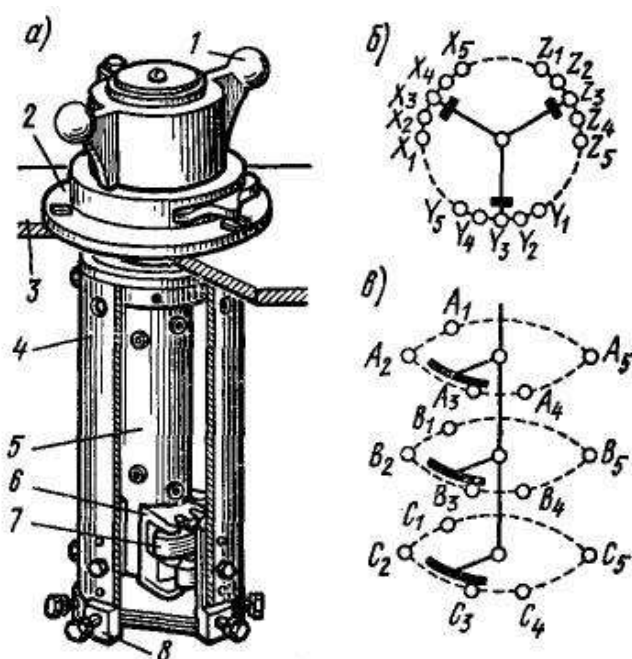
Трехфазный переключатель ответвлений (а) и схемы расположения его контактных элементов (б, в): 1 — привод, 2 — фланец колпака; 3 — крышка бака трансформатора; 4 — бумажно-бакелитовый цилиндр; 5 — бумажно-бакелитовая изоляция вала; 6 — коленчатый вал; 7 — подвижные контакты; 8 — неподвижные контакты
